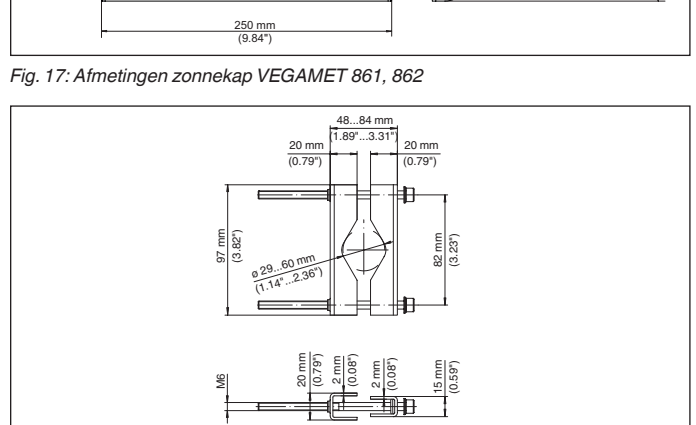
Afmetingen klemmen voor pijpmontage VEGAMET 861, 862
